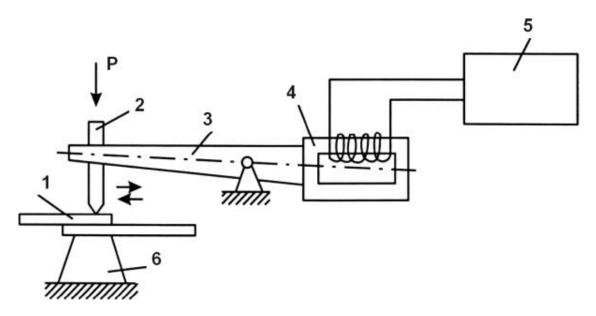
Принципиальная схема ультразвуковой сварки:
